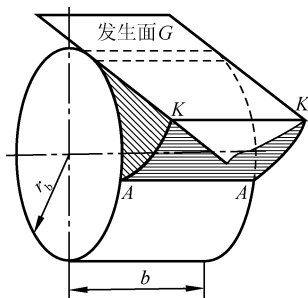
渐开线直齿圆柱齿轮齿面的形成
